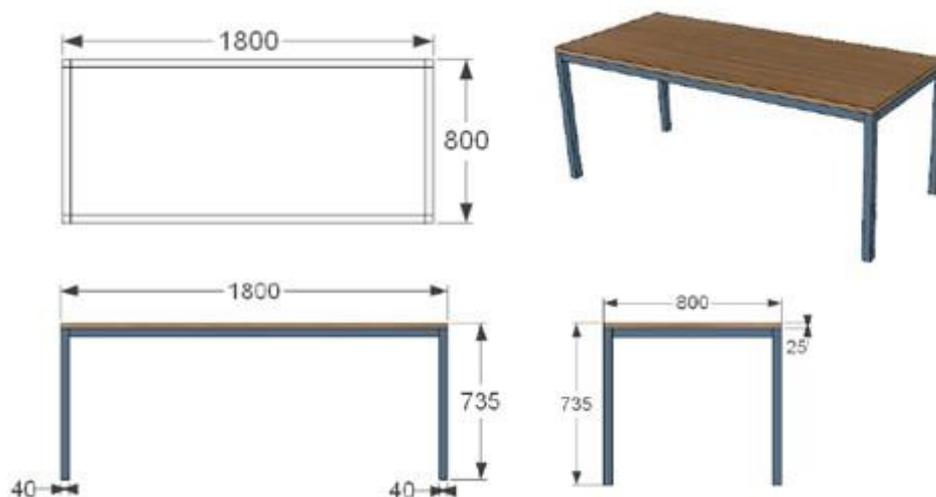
Planta baixa, vista frontal, vista lateral e perspectiva modelo item 25
